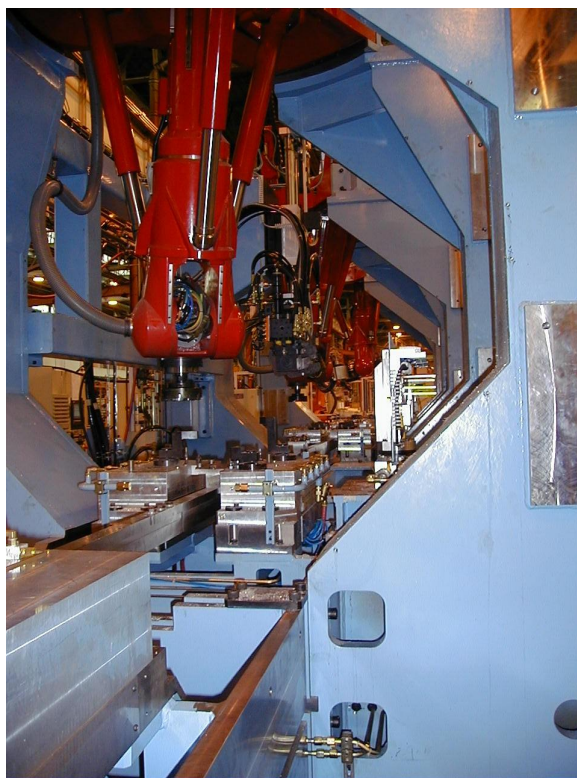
Фрезерная и сверлильная обработка моторных блоков из чугуна и алюминия. ИВАГ-моторшпиндели перемещаются по линейным направляющим.
